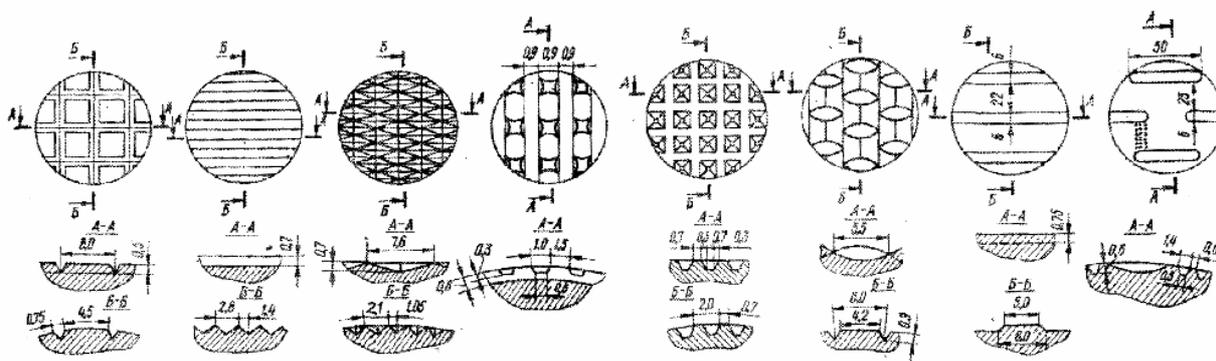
Виды рифлений на рабочих валках обжимных станков.
